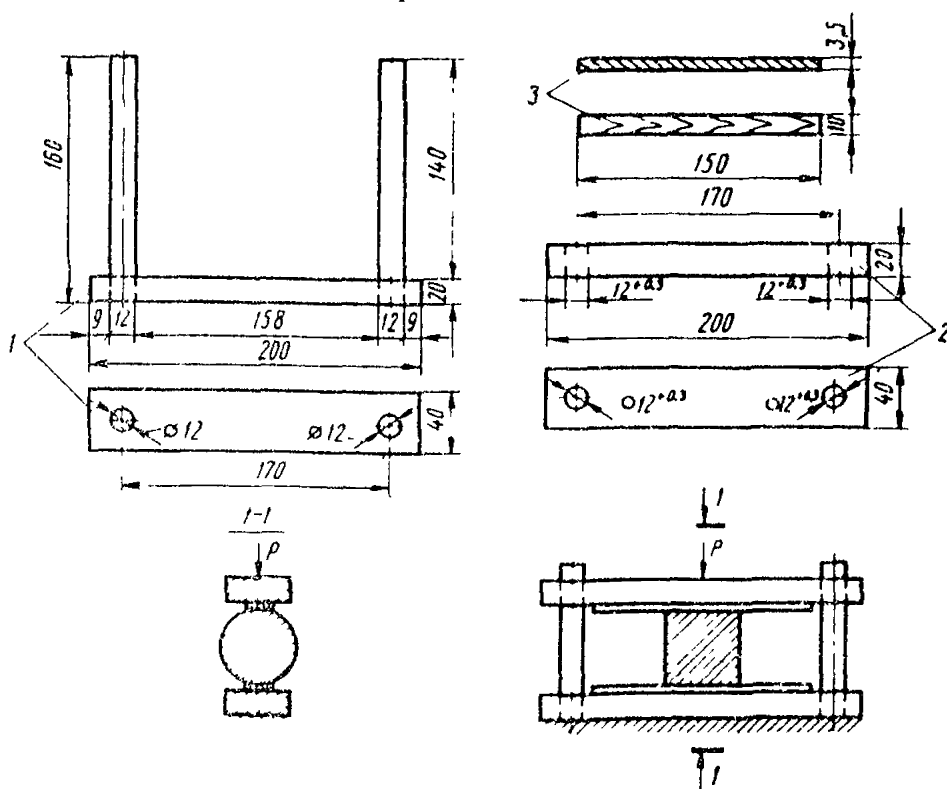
Схема испытаний образцов-цилиндров на раскол: 1 – нижняя плита с направляющими штангами; 2 – верхняя съемная плита; 3 – прокладка
